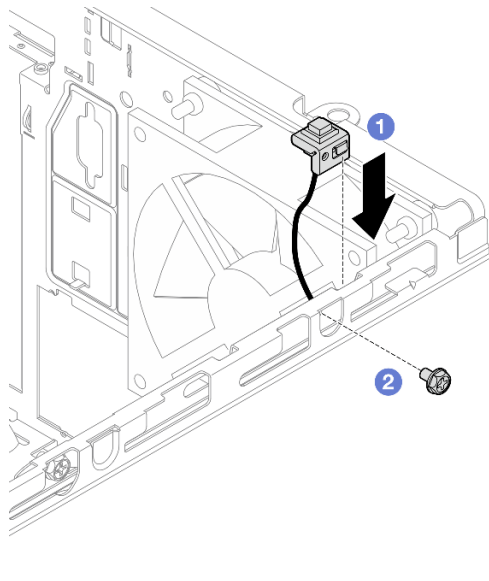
Installieren des Schalters gegen unbefugten Zugriff
